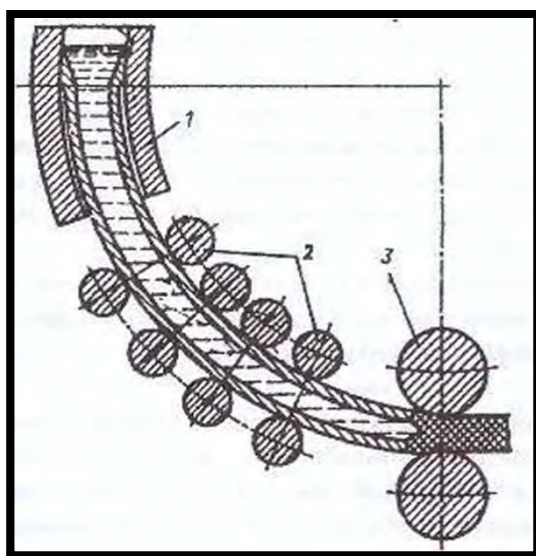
Кристаллизатор тонкослябовой конструкции, изготовленный для фирмы Nucor.
